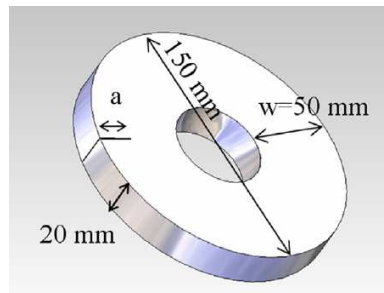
Dimensions des éprouvettes pour les essais de choc thermique (Hajjaj, 2006)
